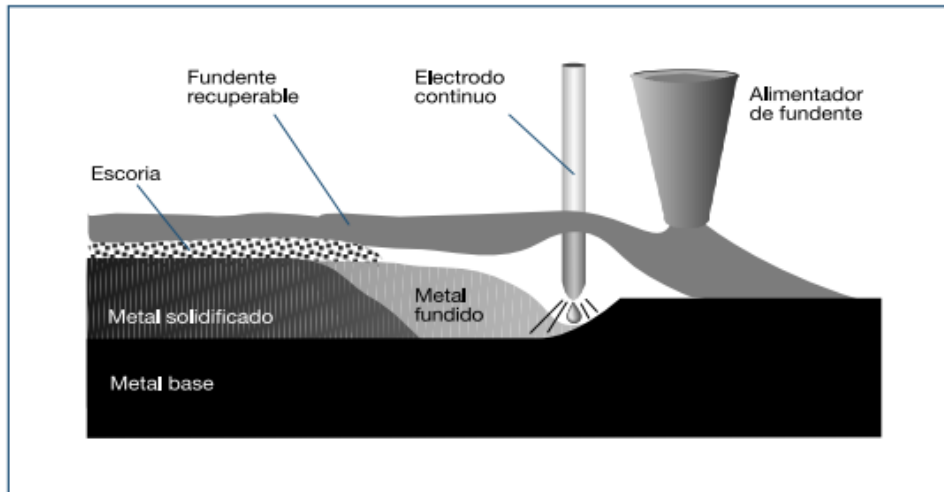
Soldadura por arco sumergido (SAW) [23].
